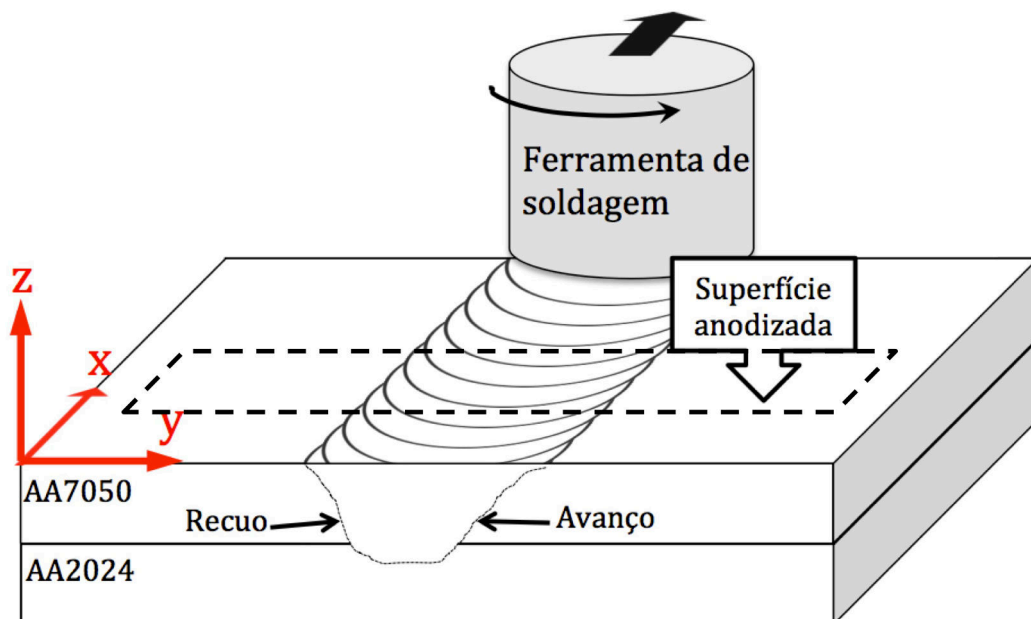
Representação da soldagem FSW da junta sobreposta 7050-2024. A área tracejada representa a região exposta ao eletrólito ($\approx 1 \text{ cm}^2$) durante as anodizações da solda.
